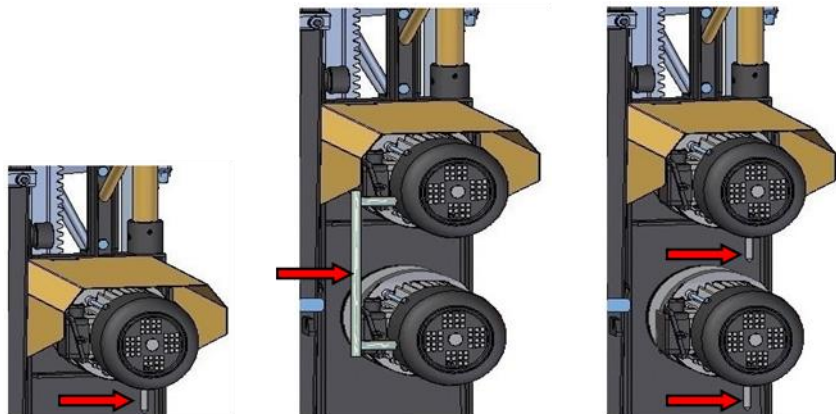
Виды механизмов для ручной разблокировки тормоза
